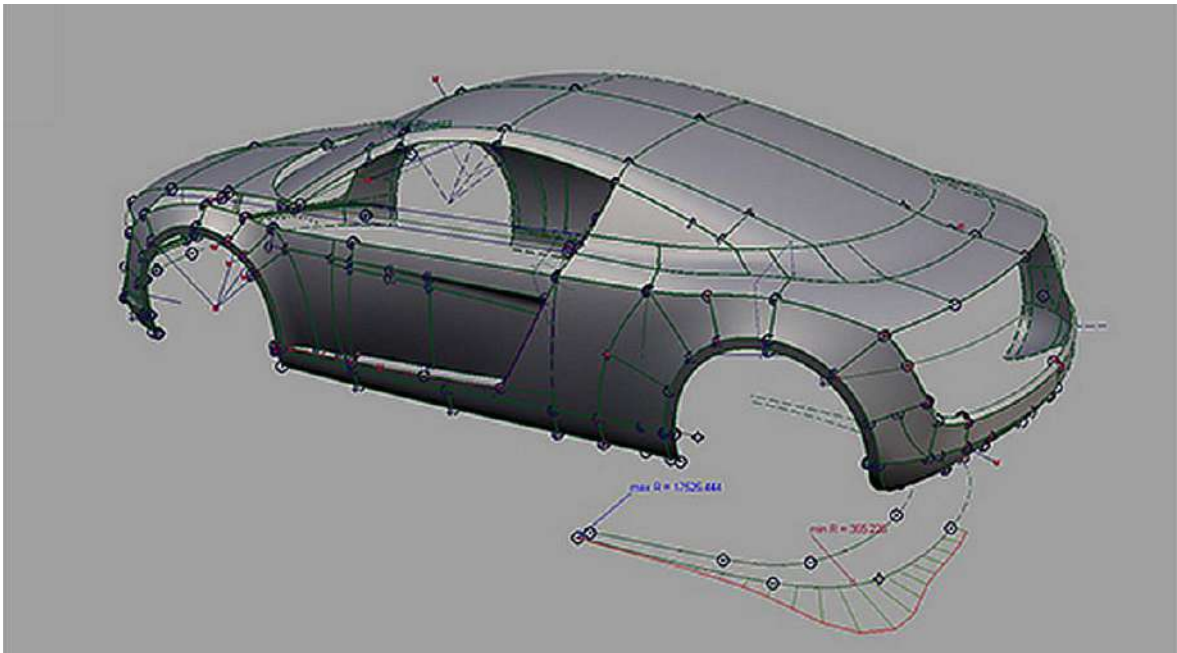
Поверхневе моделювання обшивки автомобіля
